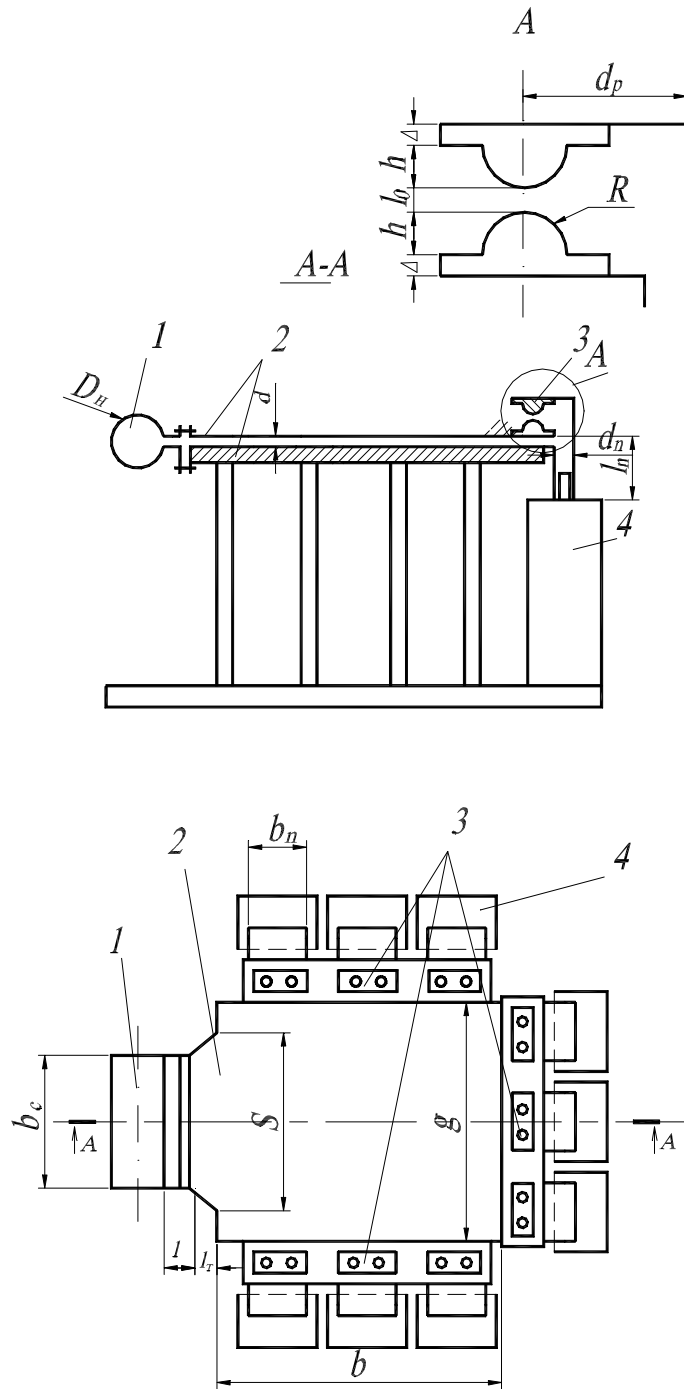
Малоиндуктивный ГИТ: 1 - нагрузка, 2 - сборные шины, 3 - разрядник, 4 - конденсатор
